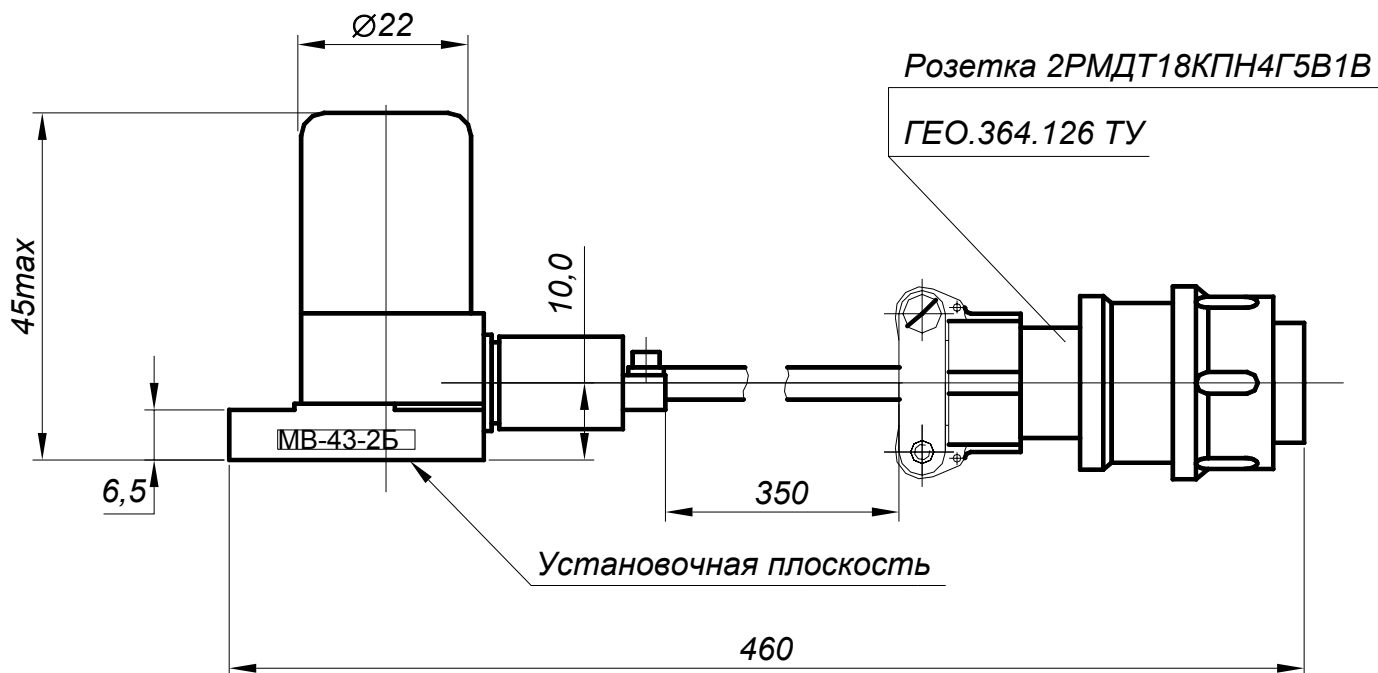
Габаритно- установочные размеры вибропреобразователя MB-43-2Б/0,35
